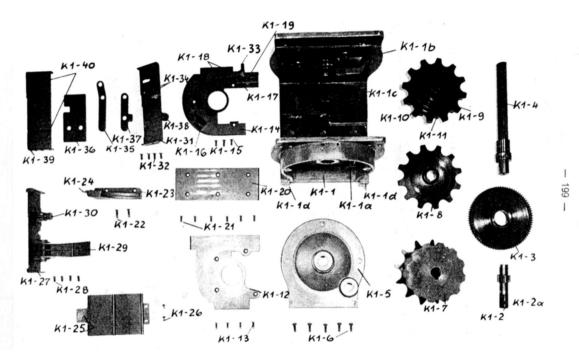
Gurtfüller 151; Gehäuse mit Getriebe, Einzelteile
